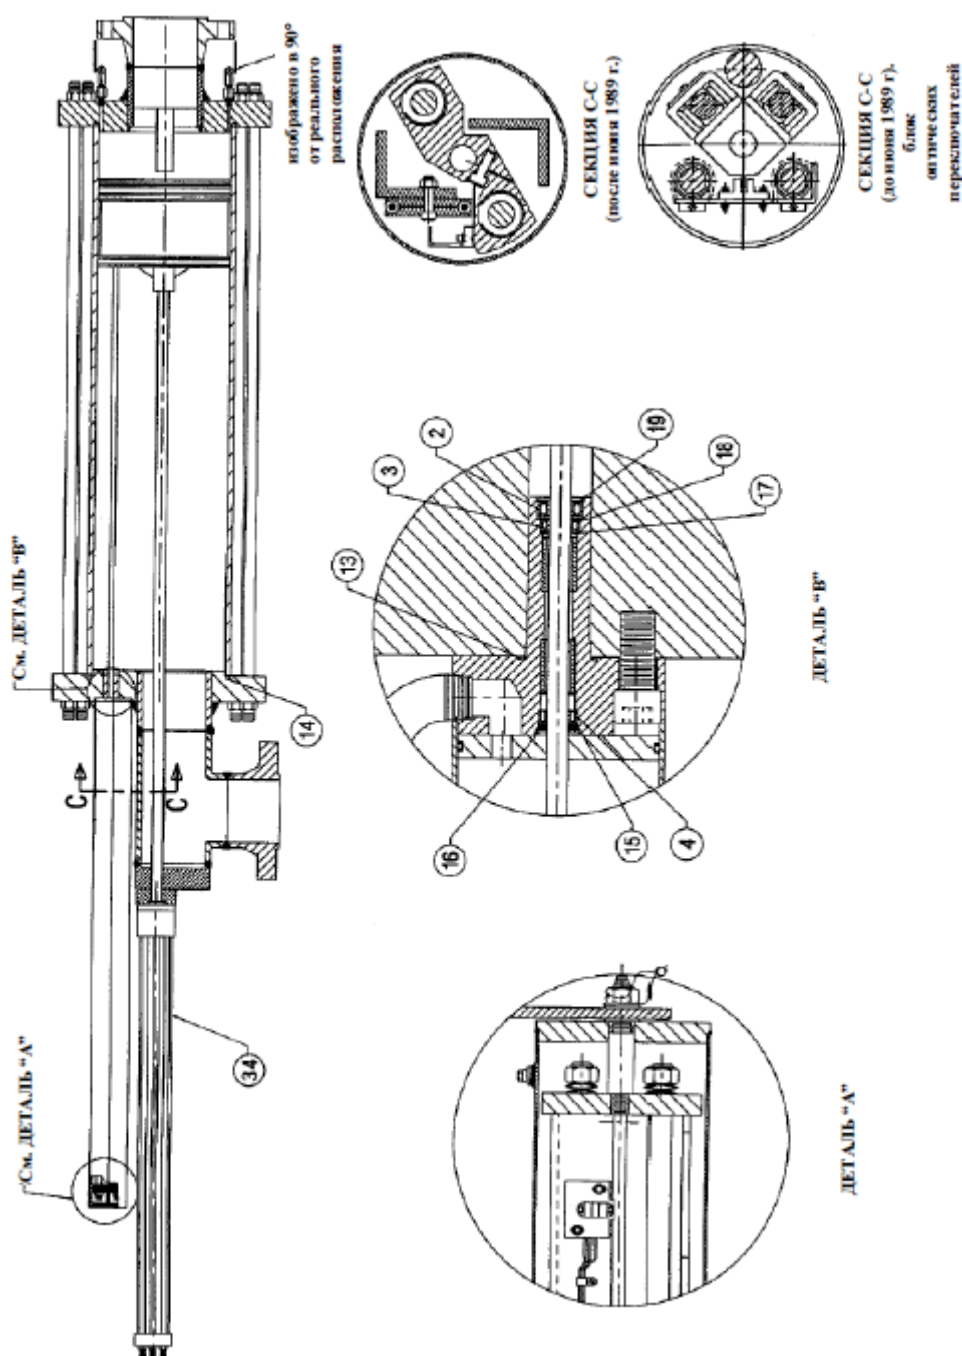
Схема расположения запчастей (измерительный цилиндр)
